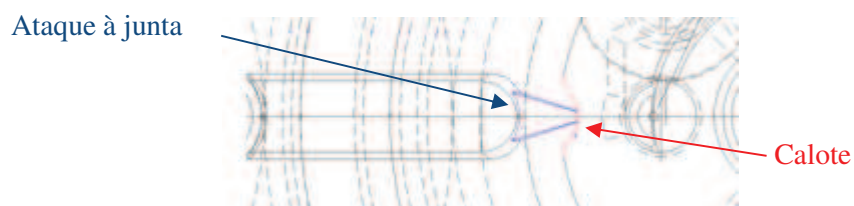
Pormenor do ataque à junta e da calote em planta (retirado do 2D).
